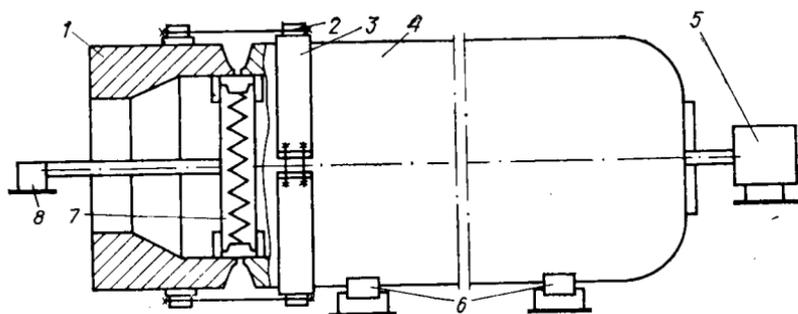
Сварка корпуса аппарата высокого давления:
